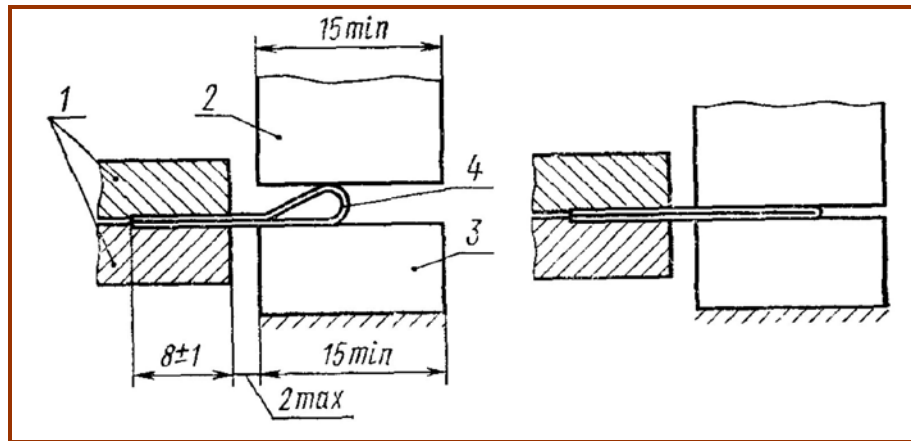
Принципова схема затискання та навантаження зразка: 1 - затискувач; 2 - пуансон для здавлювання зразка; 3 - нижня основа; 4 - випробувальний зразок
